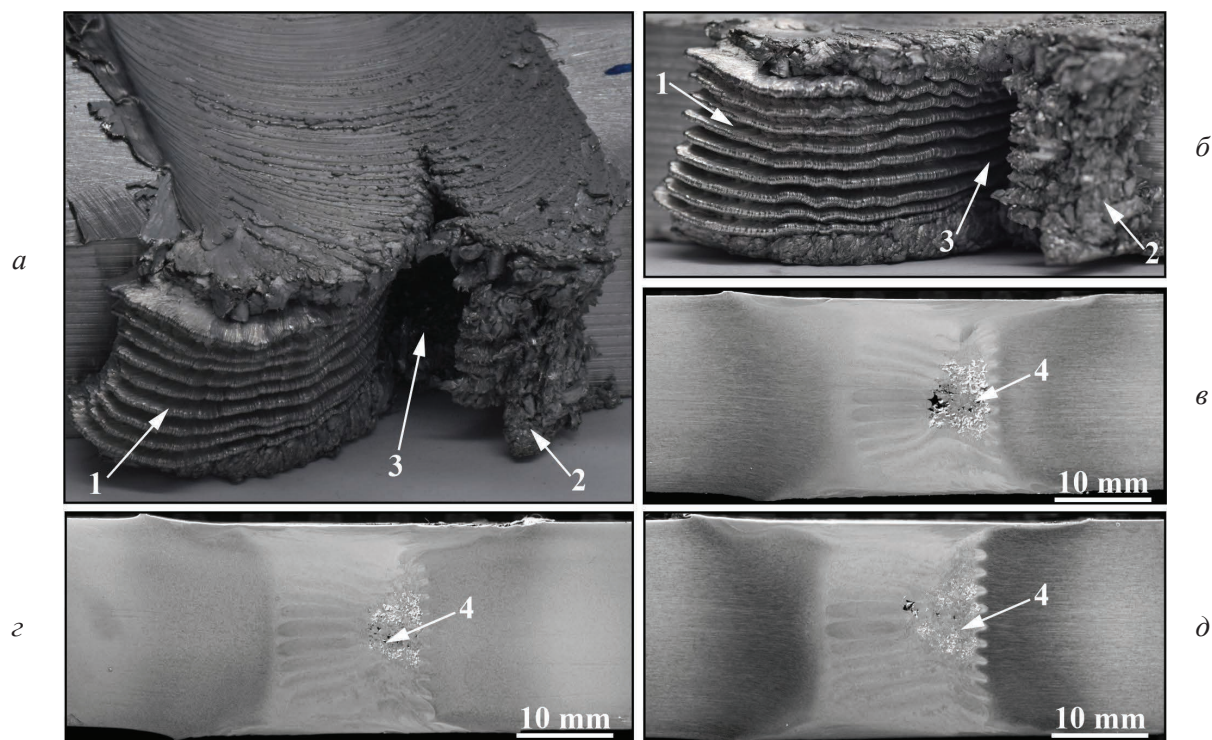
Зона входа инструмента в начале сварного соединения:
